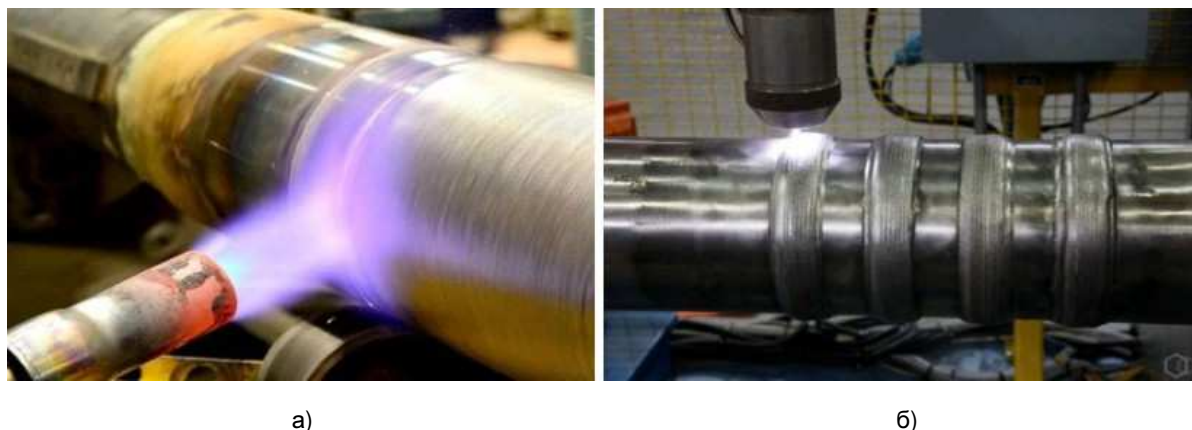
Газопламенная наплавка (а); плазменная наплавка (б)
